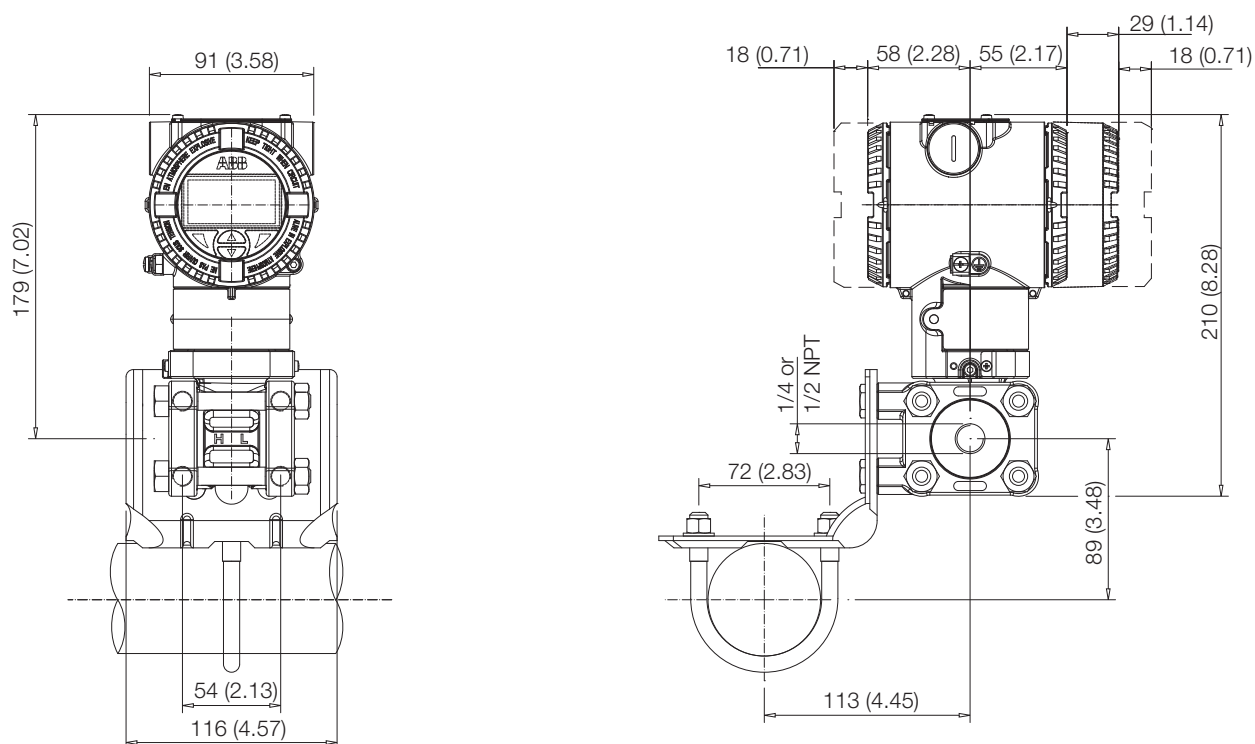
Преобразователь дифференциального давления с цилиндрическим корпусом и вкладышами Kupa, установленный на вертикальной трубе с помощью монтажного кронштейна (B2)
